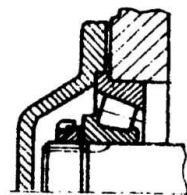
Регулировка зазоров в коническом радиально-упорном подшипнике
